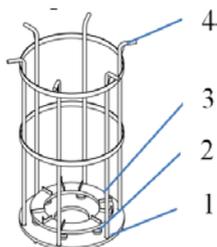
Оснастка для загрузки деталей: 1 – нижняя плита; 2 – изоляторы опорные; 3 – верхняя плита; 4 – стяжки
